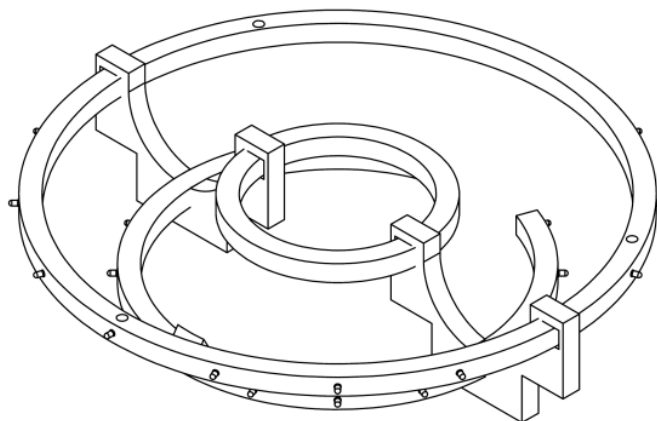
15: Vista isométrica del ensamble del espiral. Fuente: Elaboración propia.
